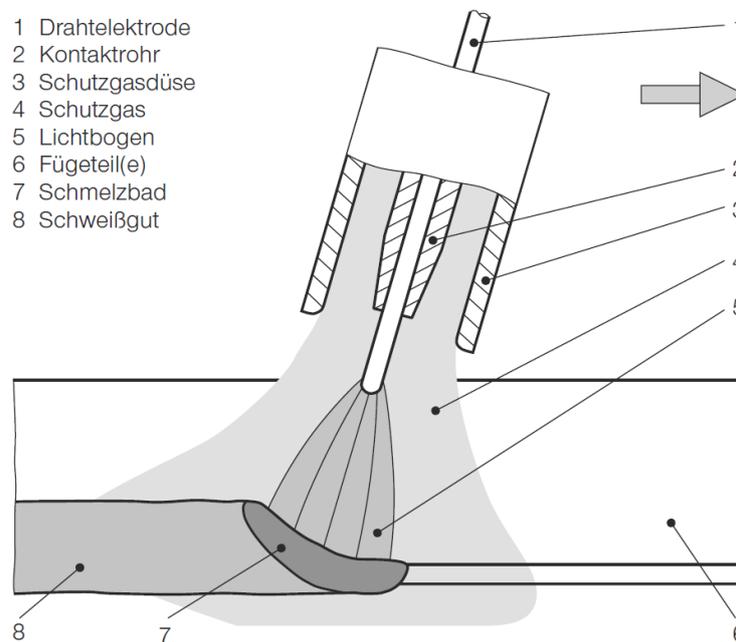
MIG/MAG-Schweißverfahren vgl. [17, p. 170]
